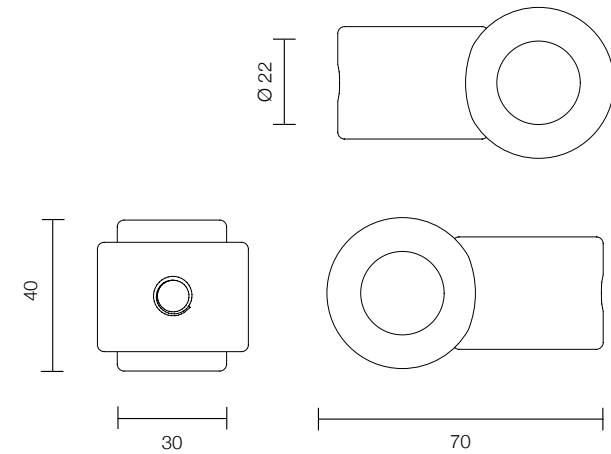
Vistas da peça de união perpendicular - frontal, lateral e superior (escala 1/2)
